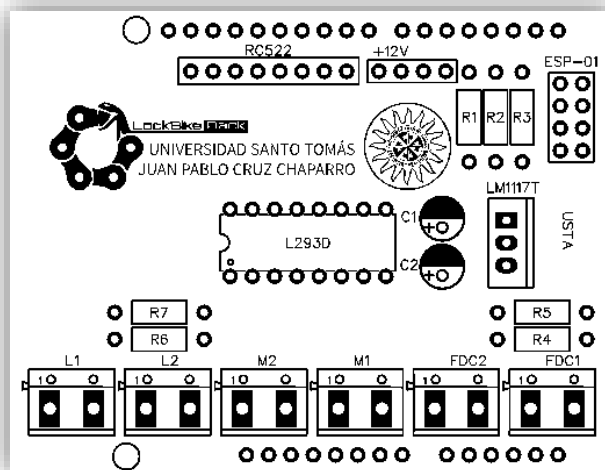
Diseño impresión física capa superior PCB, impresión – LockBikeRack
